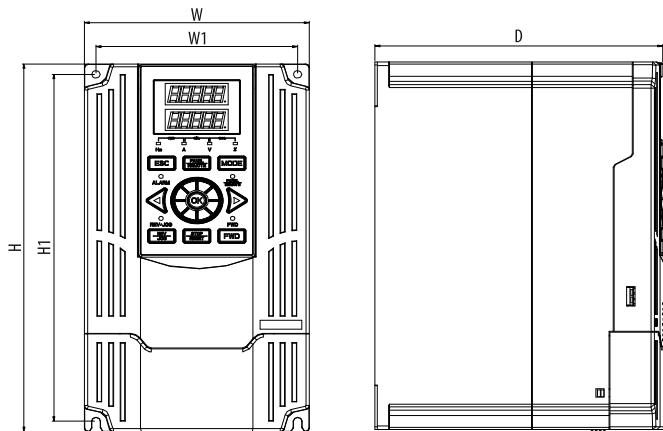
габаритные размеры AFD-E040.43B и выше (тип корпуса 2, габариты 3, 4, 5)
